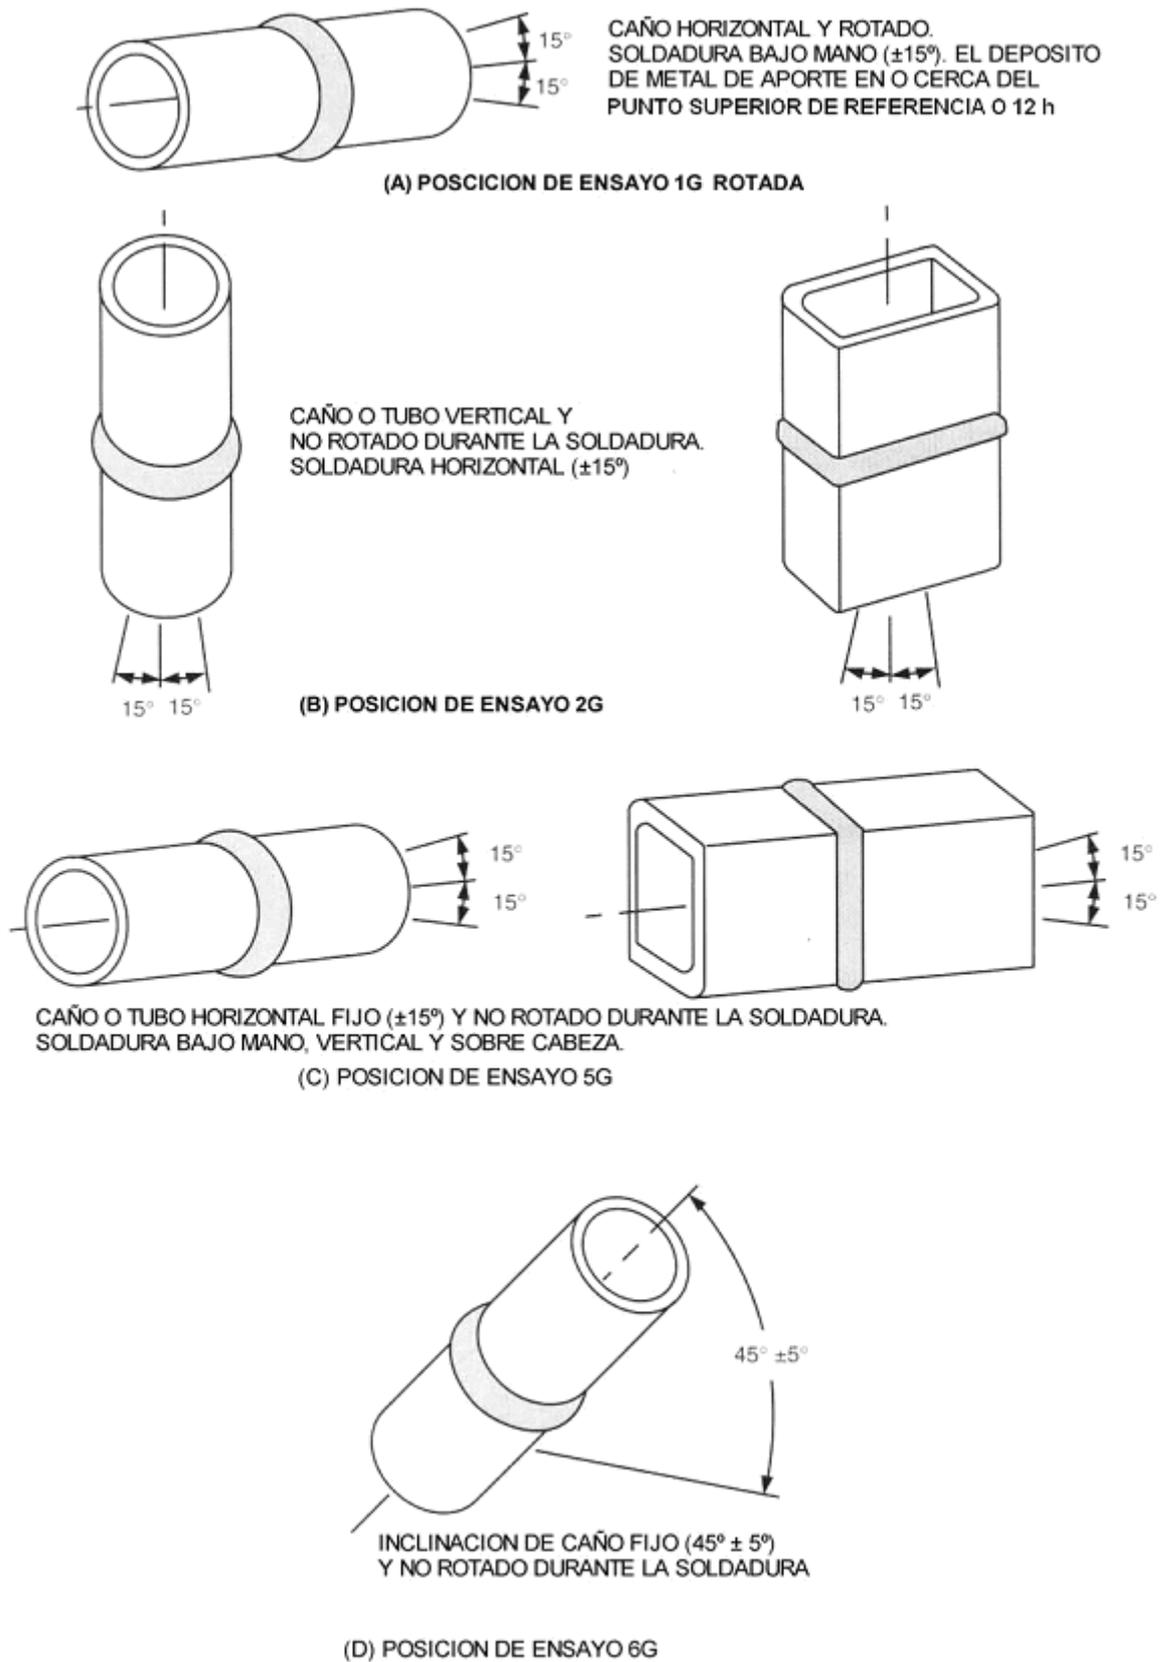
Posiciones de ensayo de caño o tubo para soldaduras con bisel
